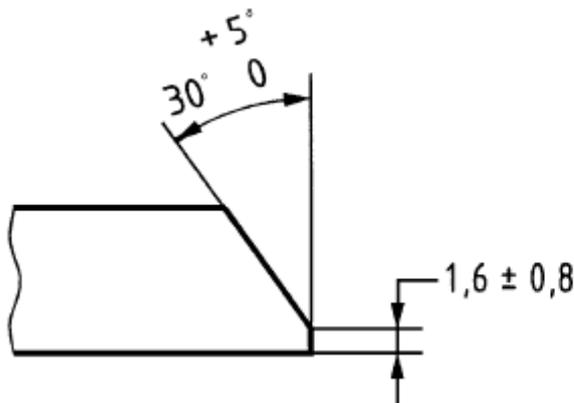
Preparación de los extremos para soldadura a tope.
